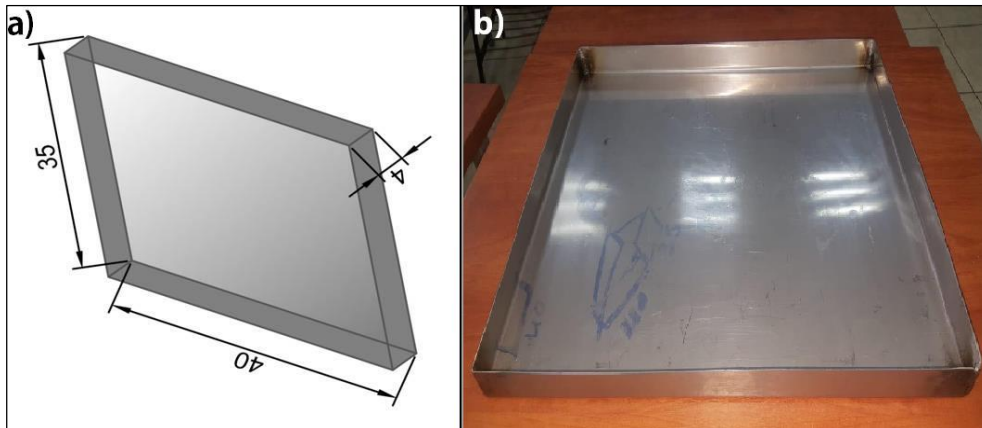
a) Diseño de la base con sus dimensiones en cm. b) Base construida.
